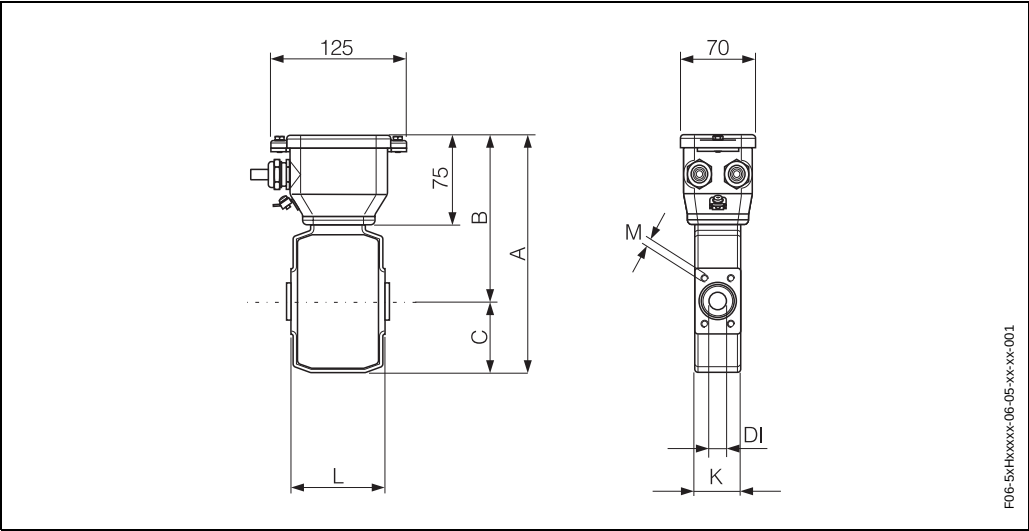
Dimensoes do Promag H / DN 2...25 (versao remota)
